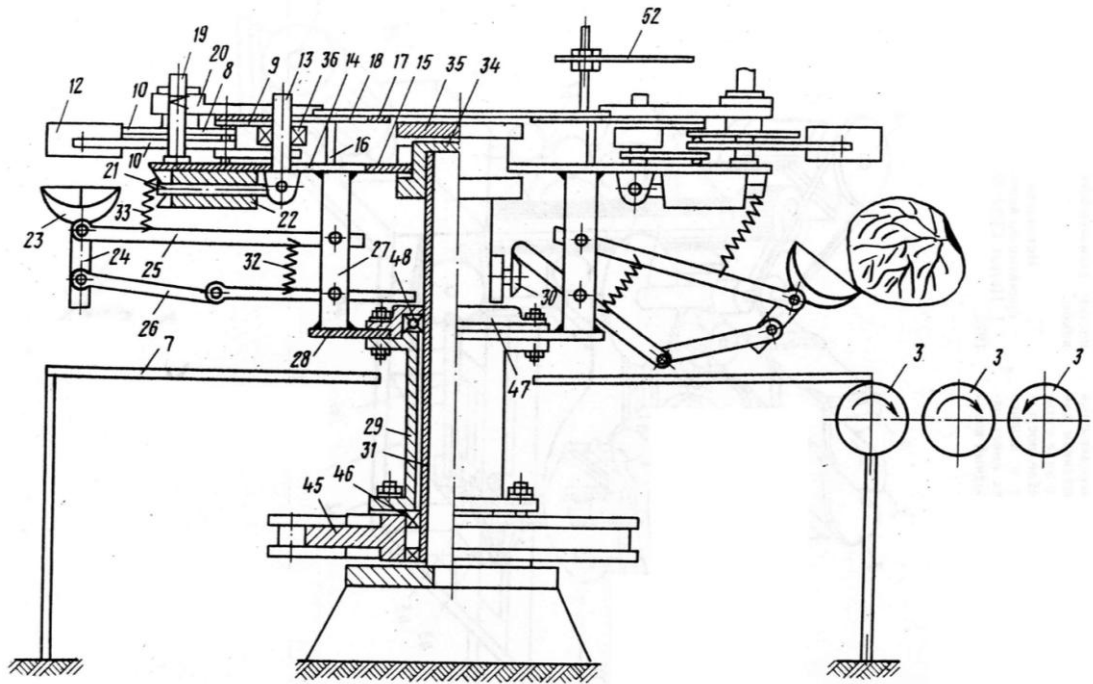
Ротор із захватами і механізмами для розміщення головок капусти, повздовжній розріз.
